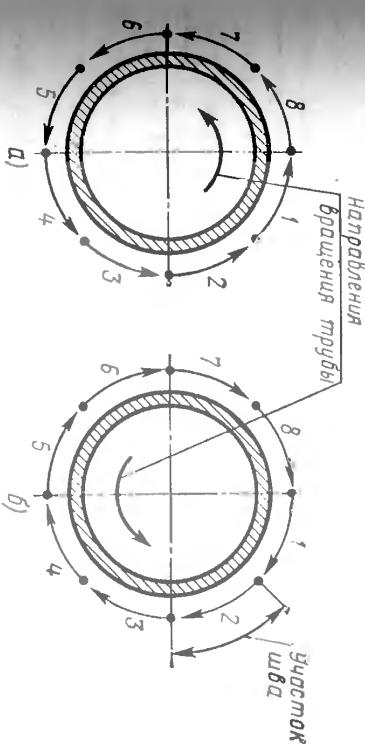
Схема сварки стыков труб большого диаметра:
